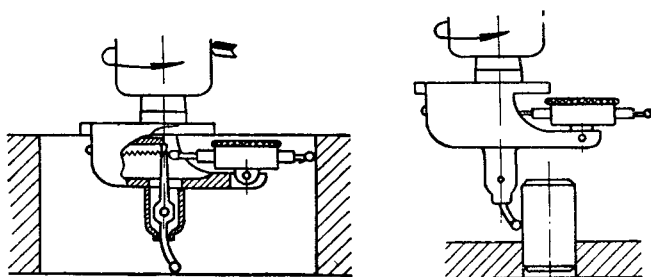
Сопряжение цилиндрической и торцевой поверхности.
